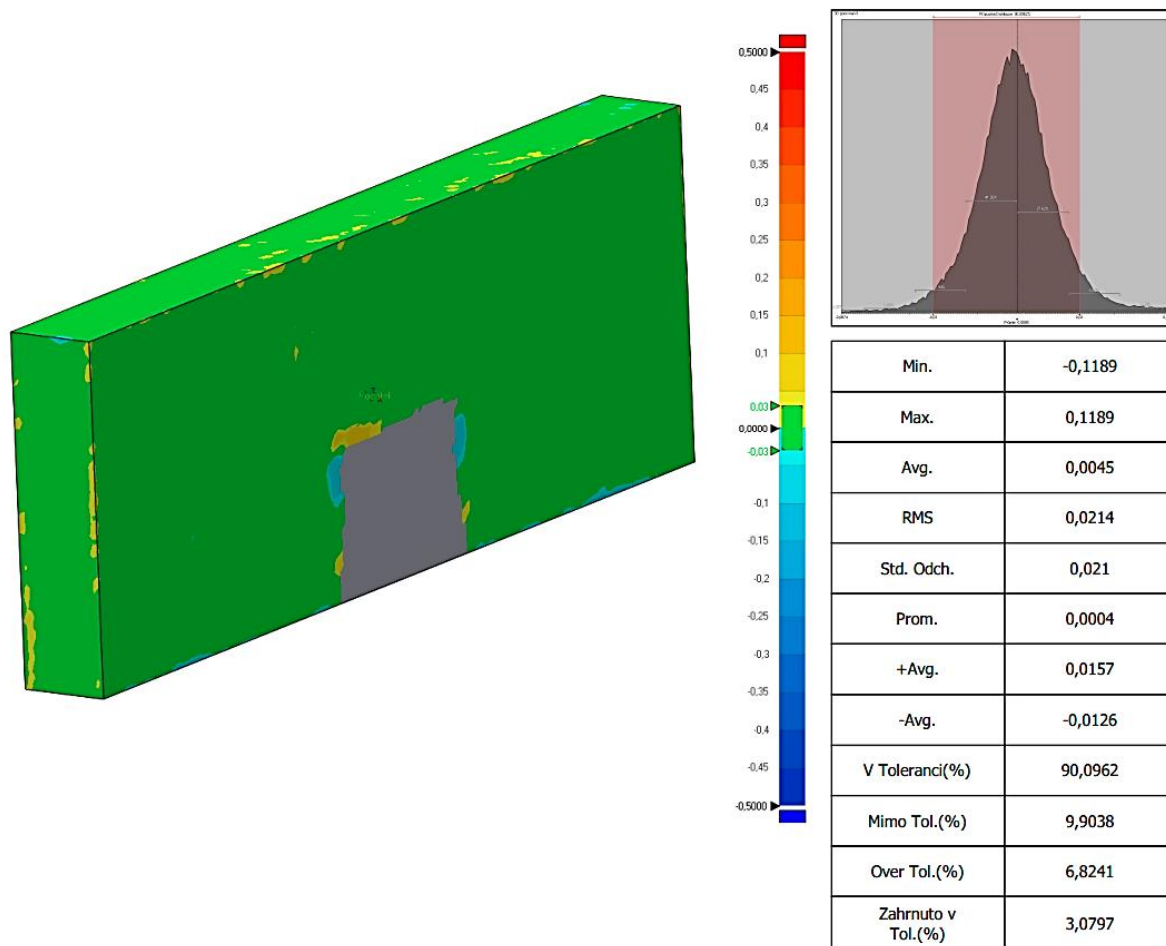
Příklad vyhodnocování odchylek na boční straně měřky
